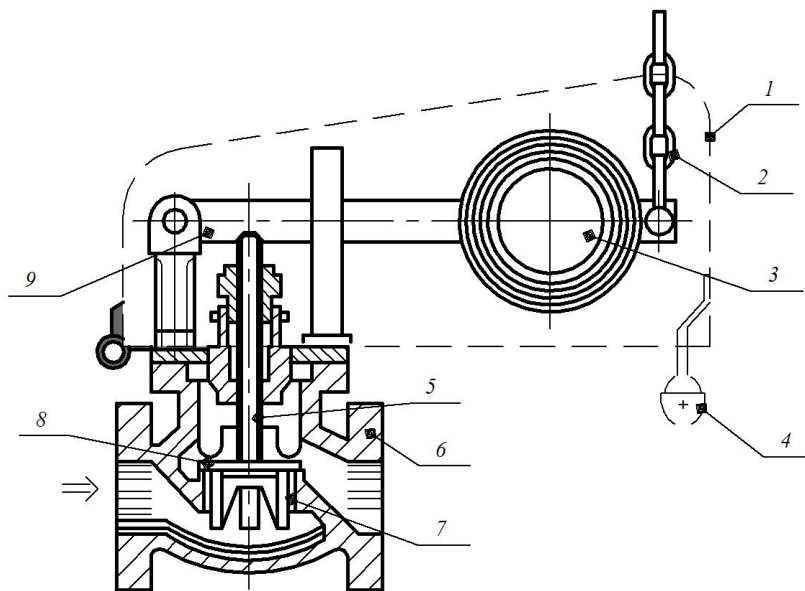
Предохранительный рычажно-грузовой клапан:
